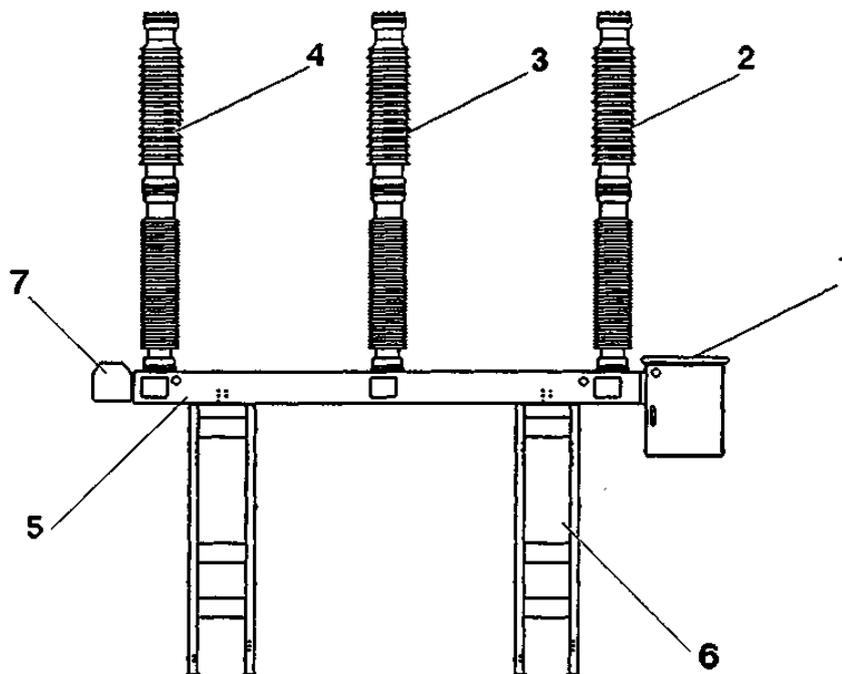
Выключатель LTB145D1/В с пружинным приводом типа ВLK 222.
